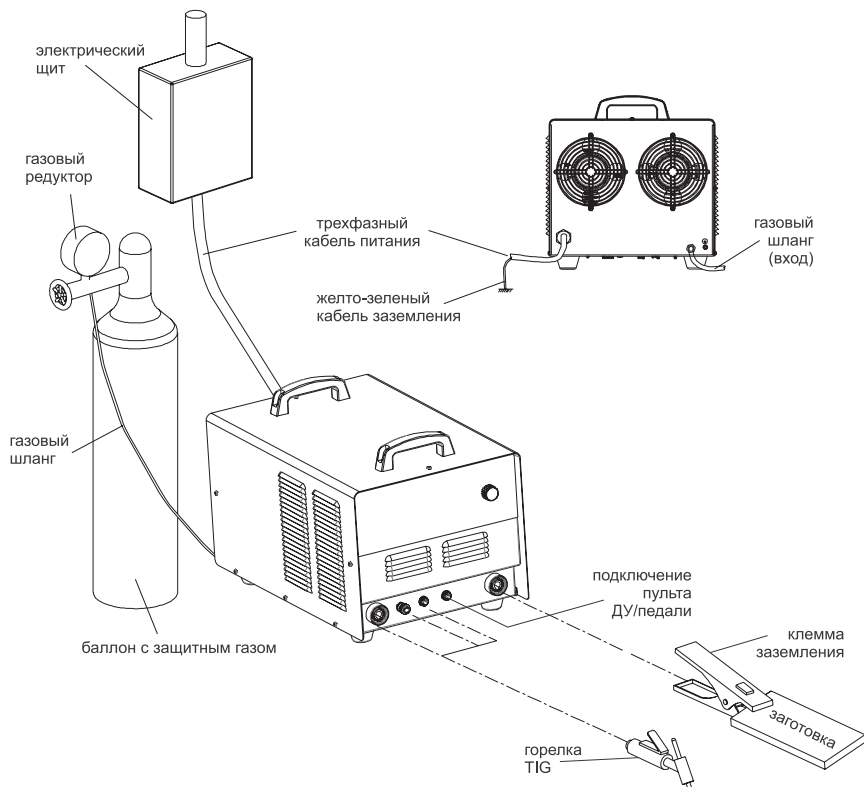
Типовая схема установки оборудования при TIG сварке
